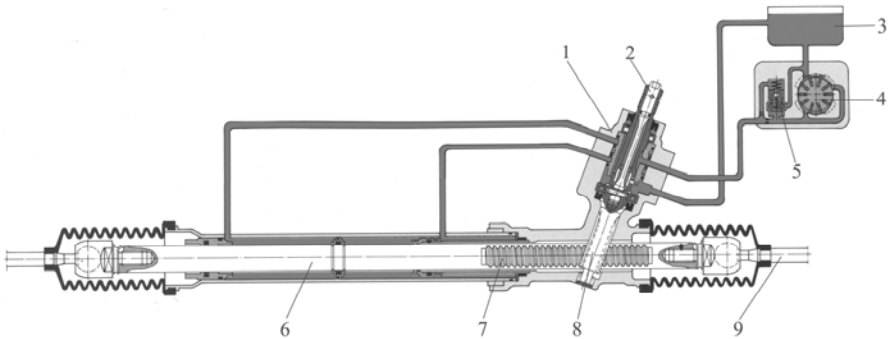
Zahnstangen-Hydraulenkung mit Drehschieberventil [3.3]. 1 Lenkventil, 2 Drehstab, 3 Ölbehälter, 4 Hydraulikpumpe, 5 Strom- und Druckregelventil, 6 Lenkzylinder, 7 Zahnstange, 8 Antriebsritzel, 9 Spurstange
